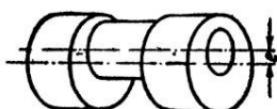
Втулка с буртами, расположенные эксцентрично относительно отверстия.
